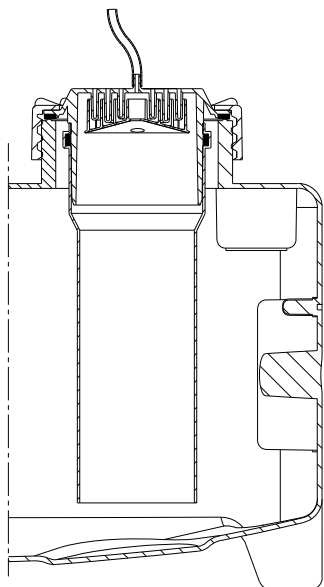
Крышка с резьбой и шланг, трубка DN 100 и уловитель конденсата
